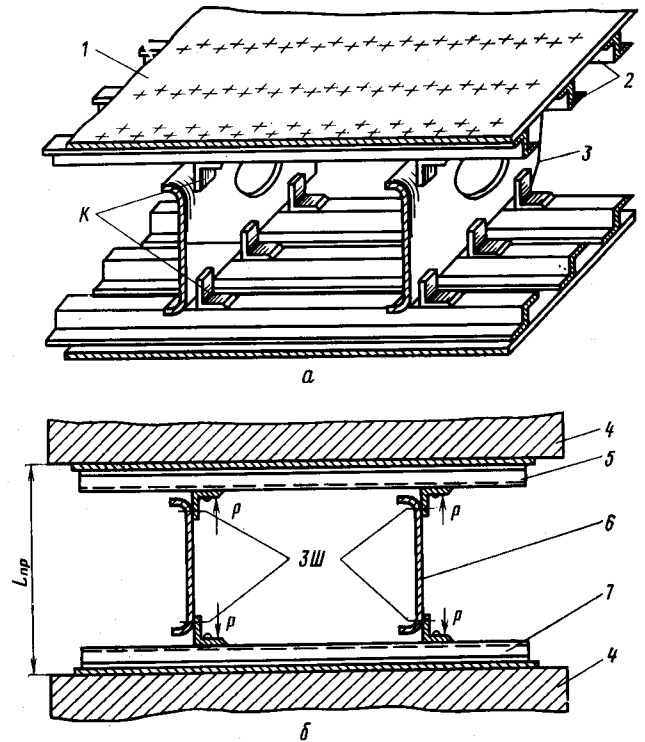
Сборка кессона крыла в приспособлении:
